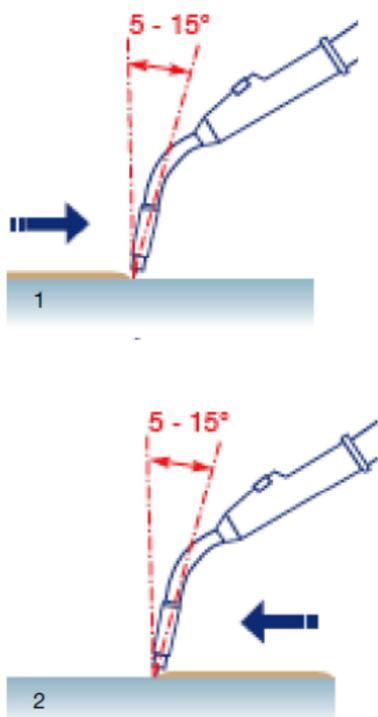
Сварочная горелка имеет наклон в направлении продольной оси шва. 1 – сварка углом назад. 2 – сварка углом вперед
